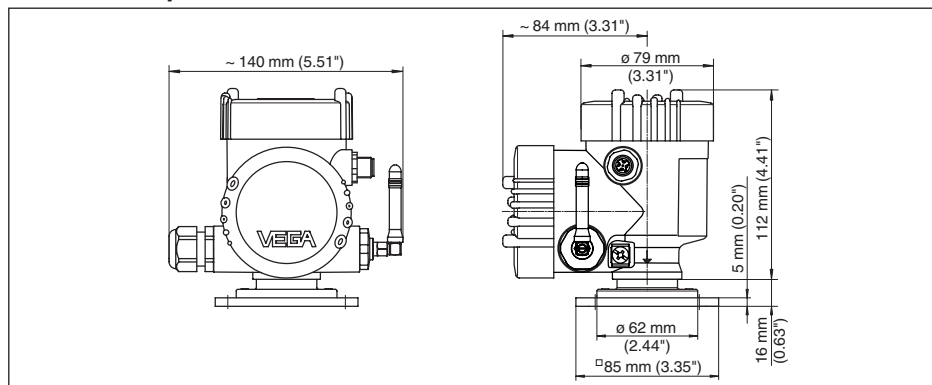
Размеры PLICSMOBILE T61 с пластиковым корпусом
